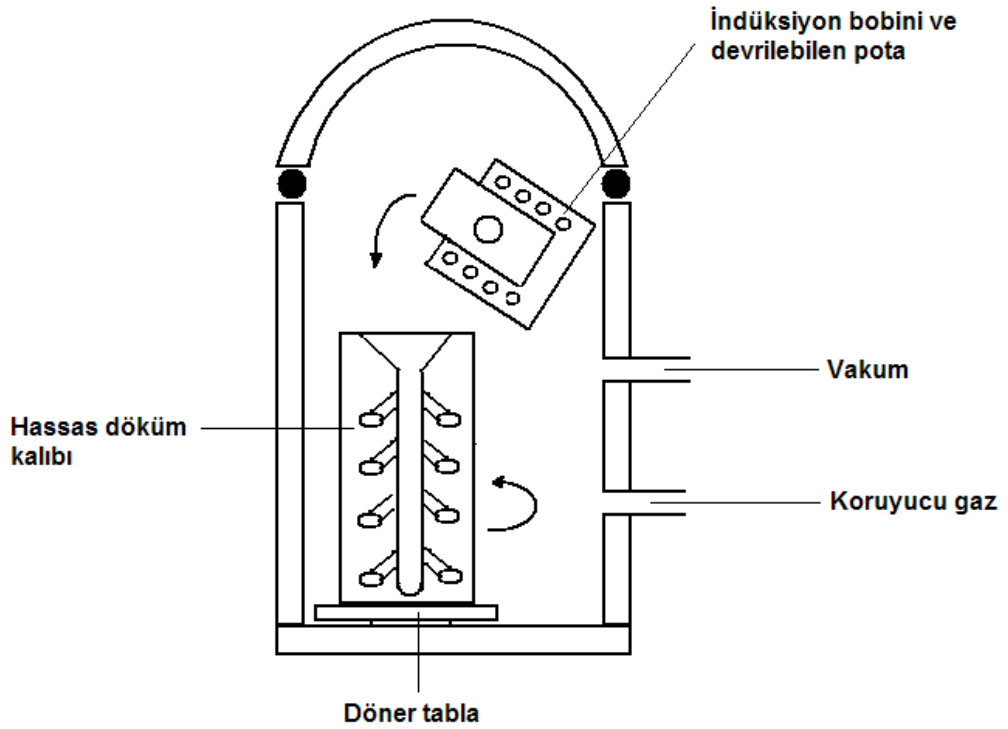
21 Vakum indüksiyon mikro döküm makinesi
